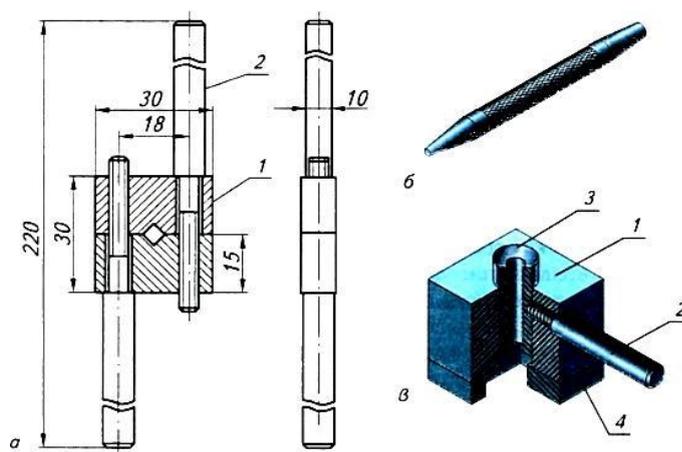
Способы представления изделий, выполненных на токарном и фрезерном станках: а — сборочный чертеж воротка: 1 — зажим; 2 — ручка; б — технический рисунок пробойника; в — технический рисунок кондуктора для сверления отверстий: 1 — корпус; 2 — ручка; 3 — втулка; 4 — основание
